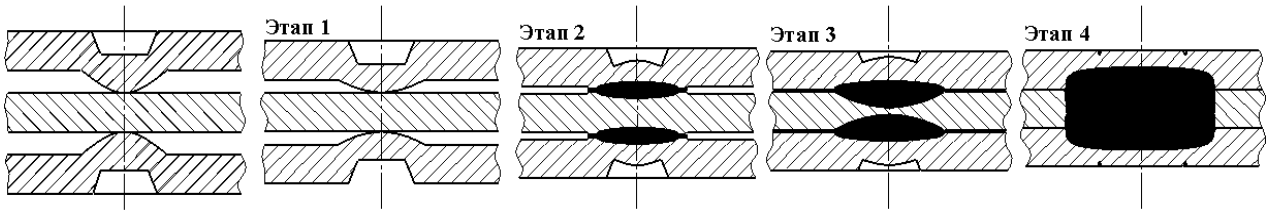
Упрощенная схема контактной рельефной сварки
